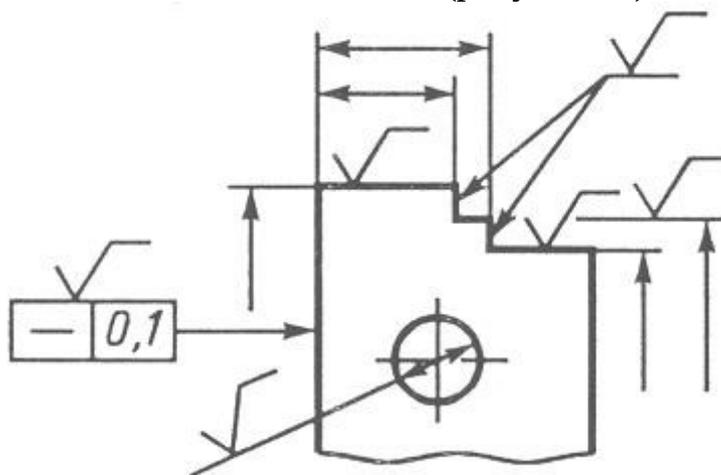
Обозначение шероховатости поверхности на изображении детали
